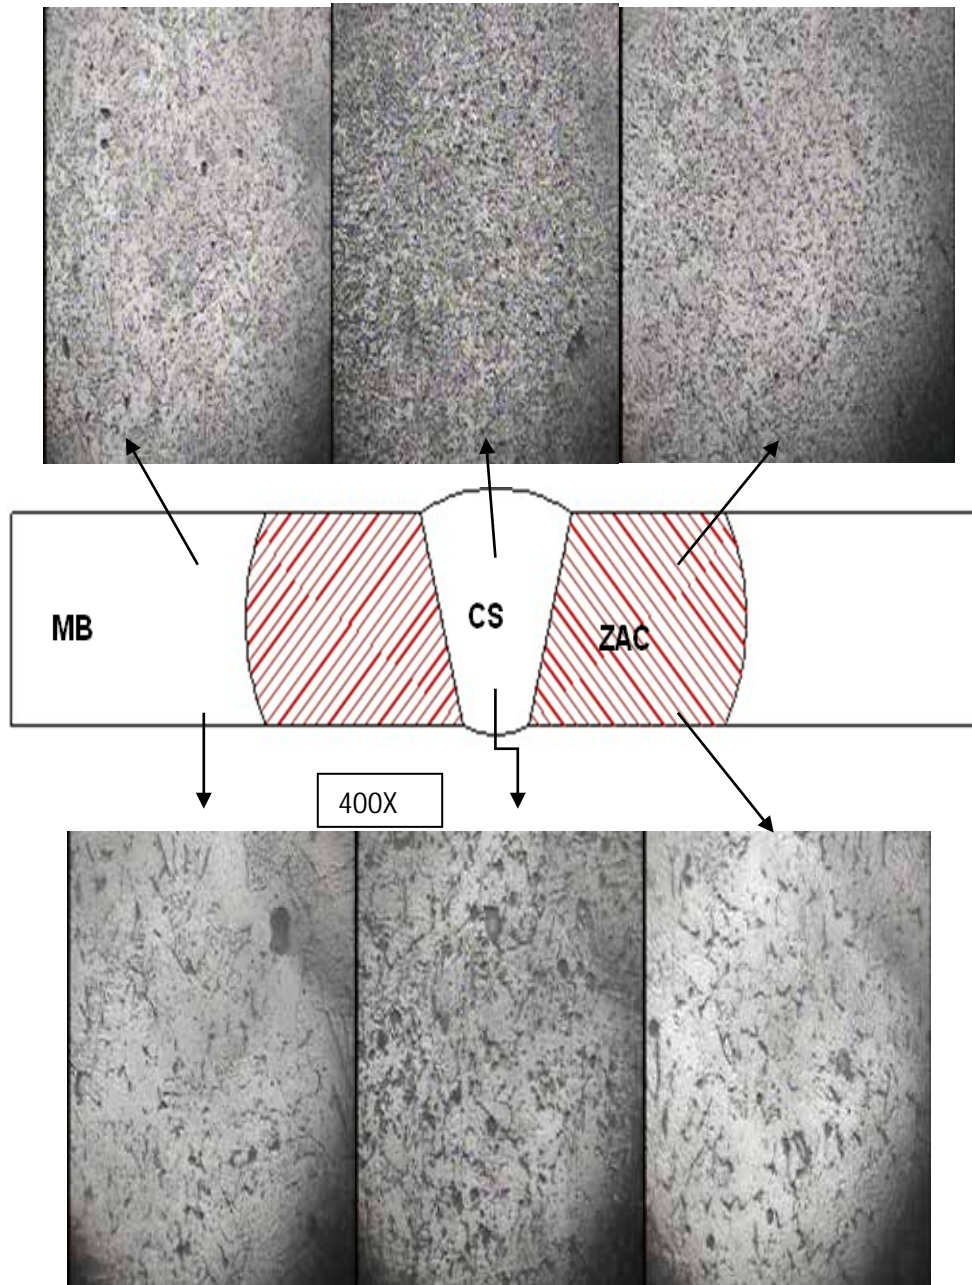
Probeta soldada con E-7018 a 150 Amp.
